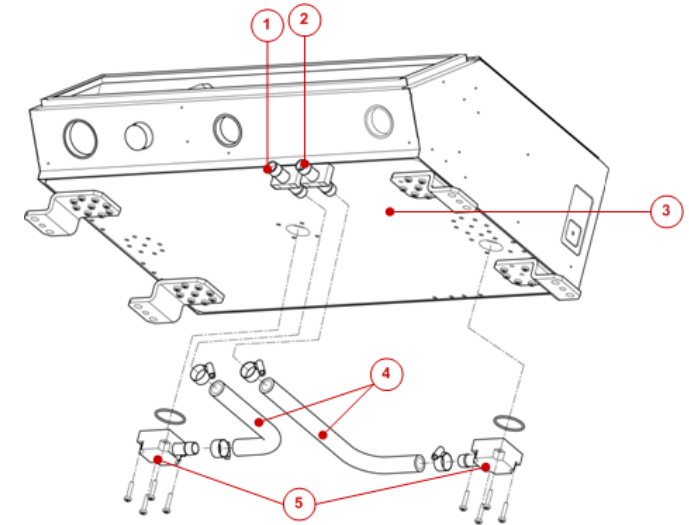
Explosionszeichnung Kühlsystem / Exploded view cooling system
